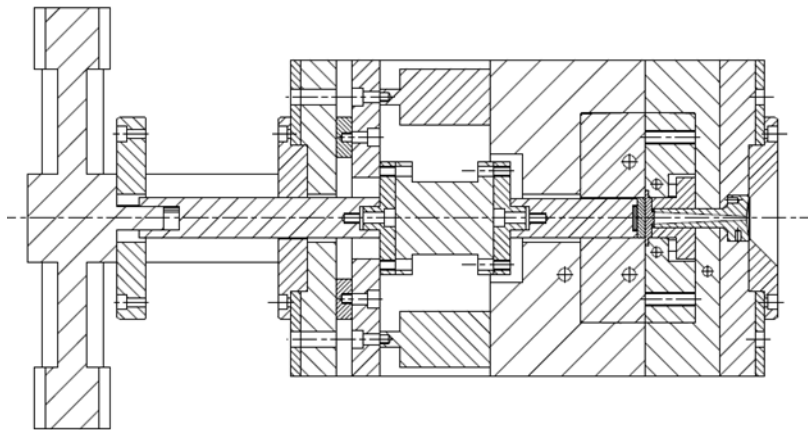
Querschnitt durch die Werkzeugkonstruktion des Entformungskraftwerkzeugs
